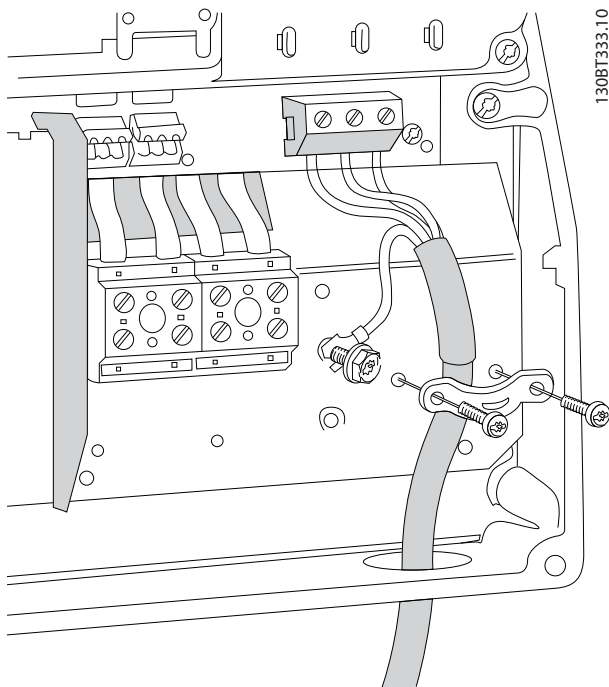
Подключение двигателя для корпусов B1 и B2
